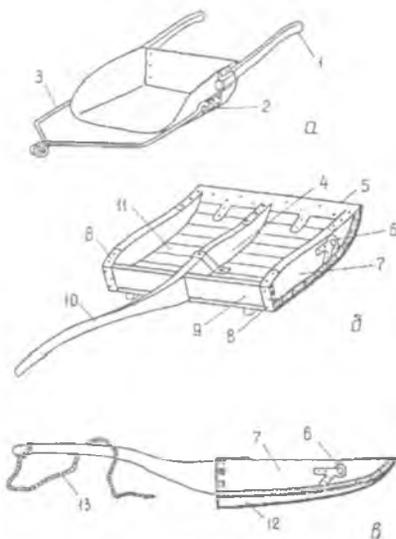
Конные лопаты: а - металлическая; б - лопата в перспективном виде; в - вид сбоку
